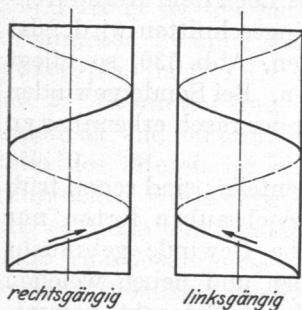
Rechts- und linksgängige Schraubenlinien.
